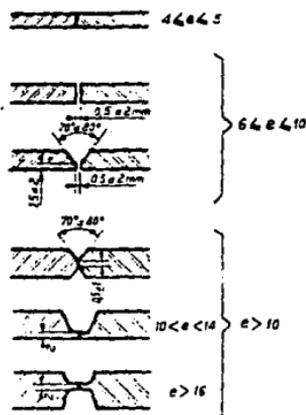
Preparación de los bordes para la soldadura MIG.
